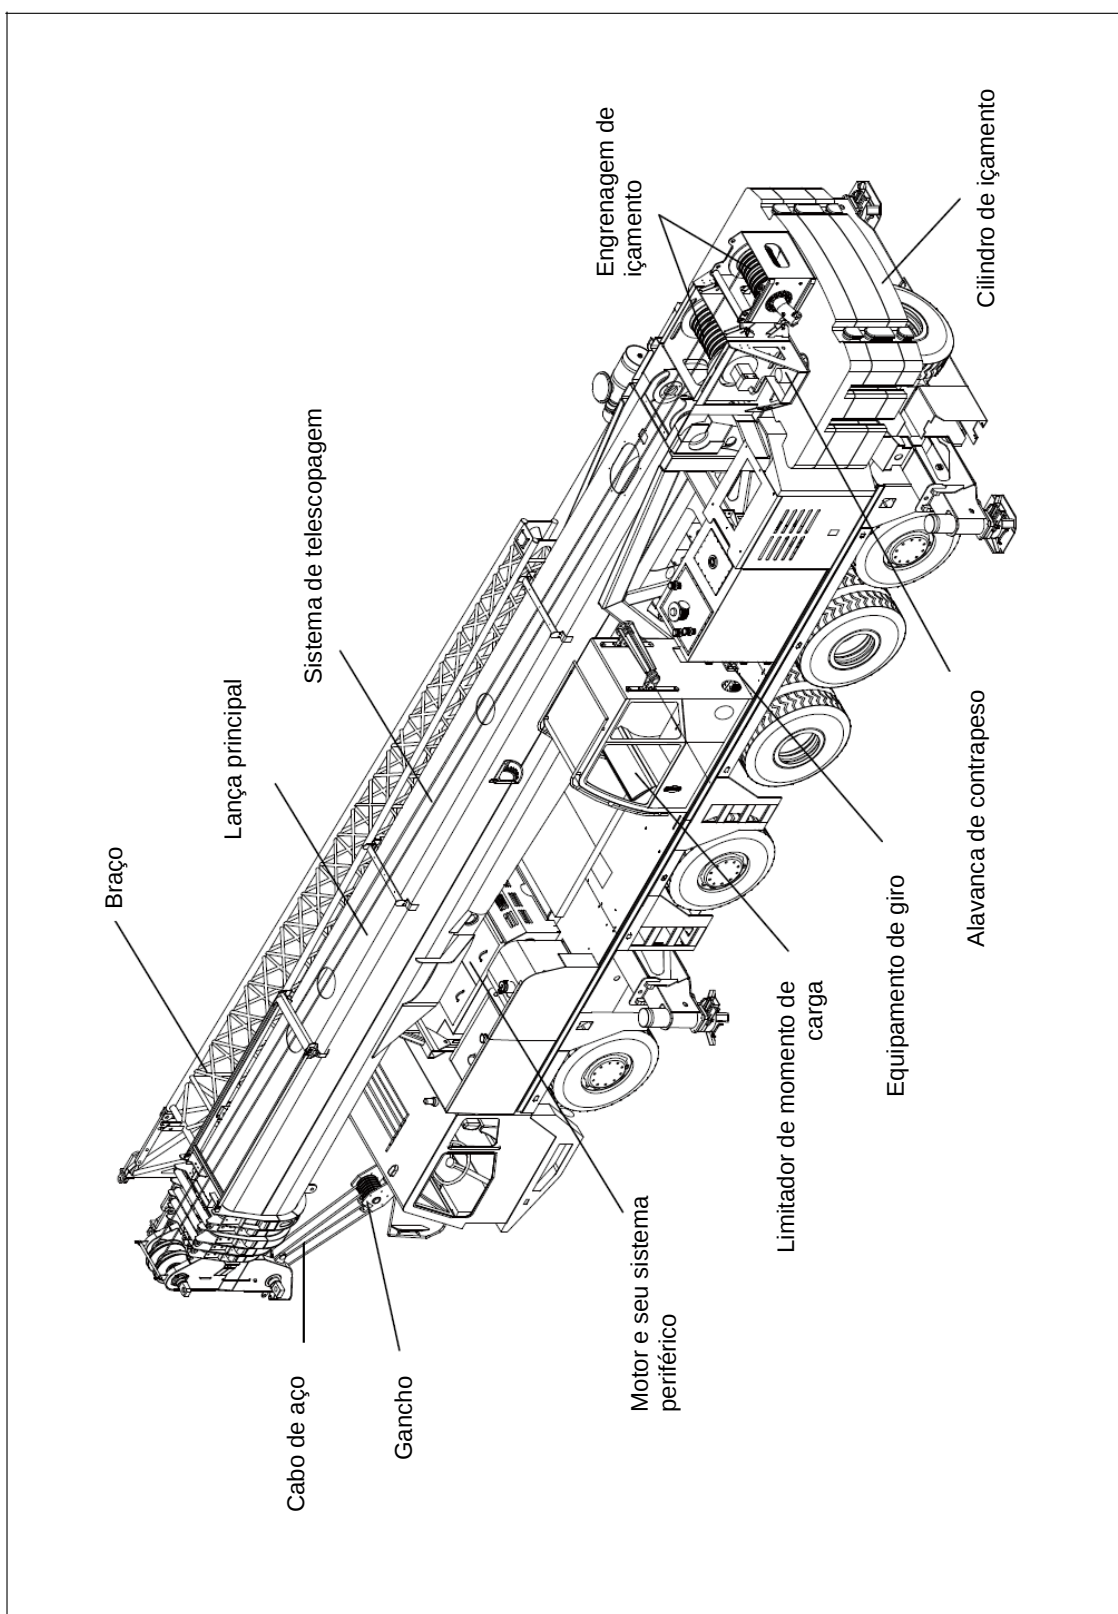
Pontos de inspeção e manutenção, superestrutura
